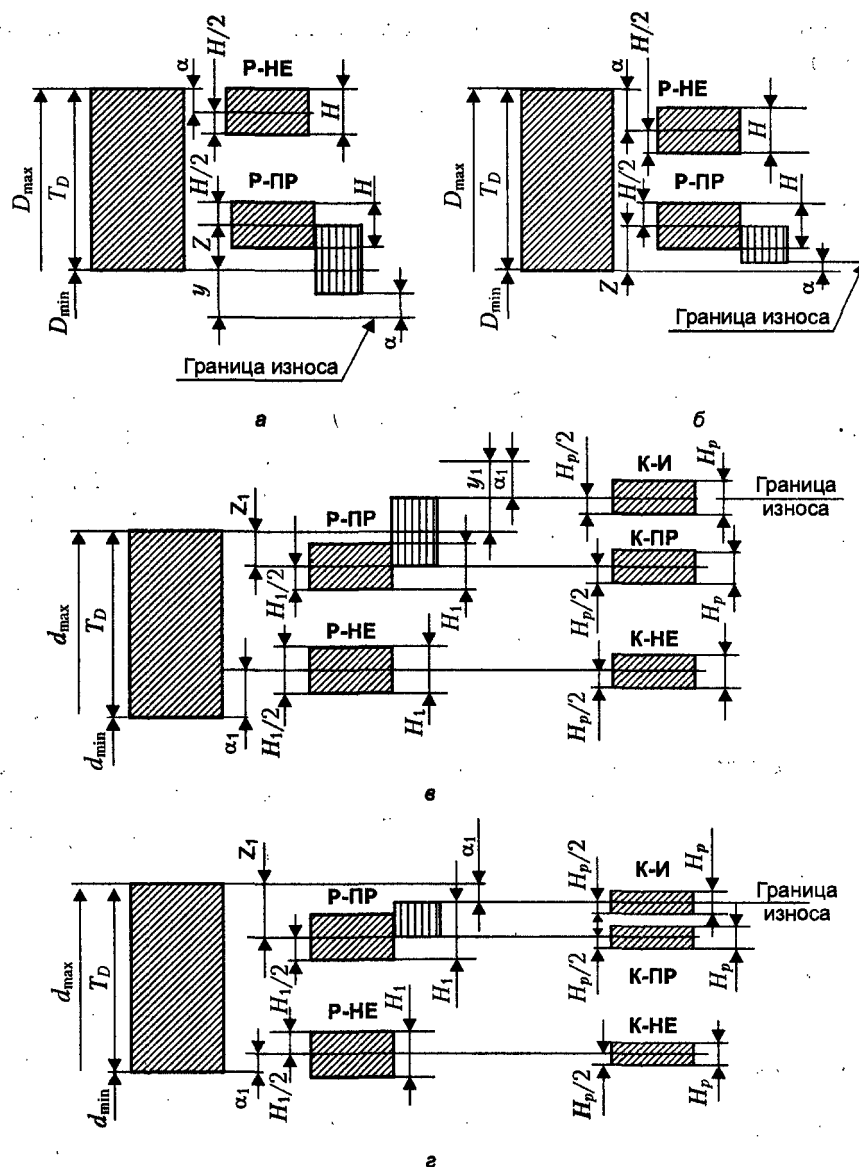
Схемы расположения допусков калибров для номинальных размеров до 180 мм: а — для отверстий IT6–IT8; б — для отверстий IT9–IT17; в — для валов IT6–IT8; г — для валов IT9–IT17
